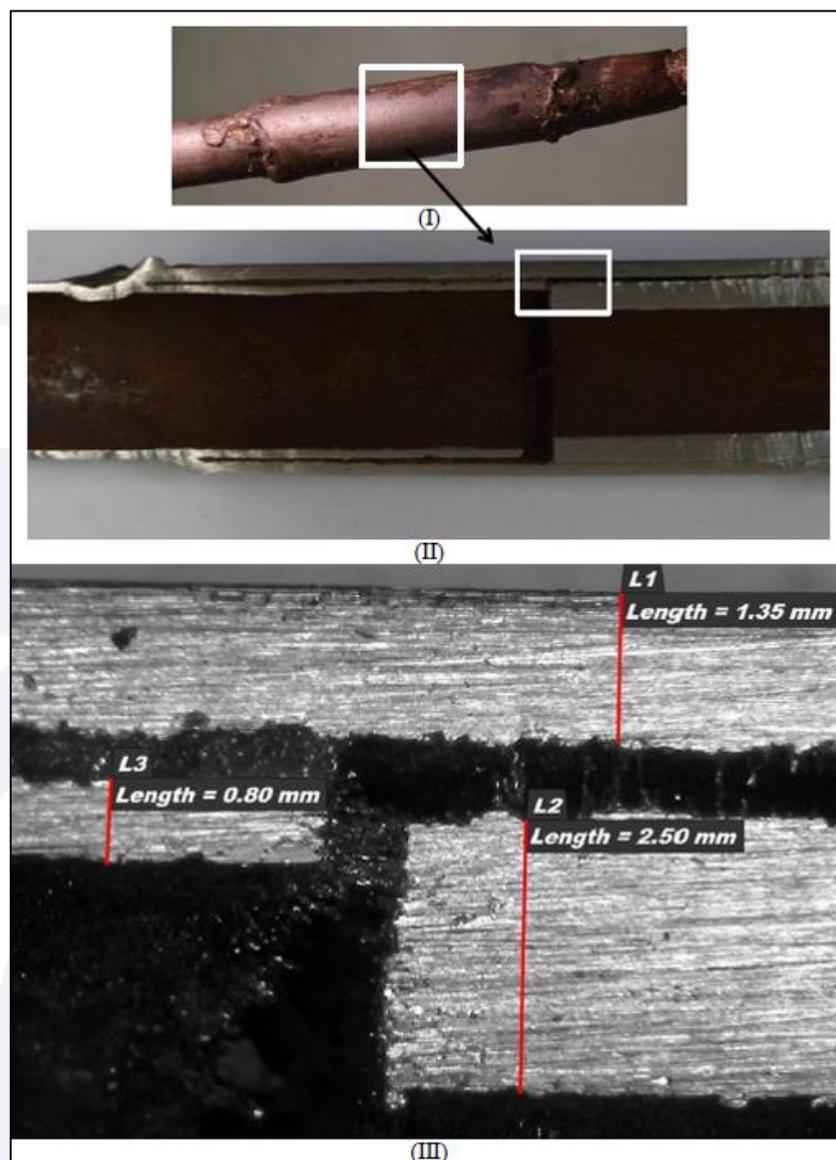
Vista interna do tubo da treliça inferior direita mostrando as espessuras dos tubos soldados.
